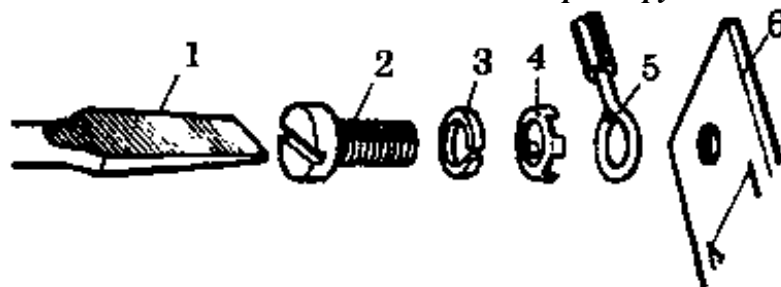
Присоединение алюминиевой жилы к плоскому выводу электрического аппарата: 1-отвертка; 2-винт; 3-пружинная шайба; 4-шайба-звездочка; 5-алюминиевая жил; 6-контактный вывод.
